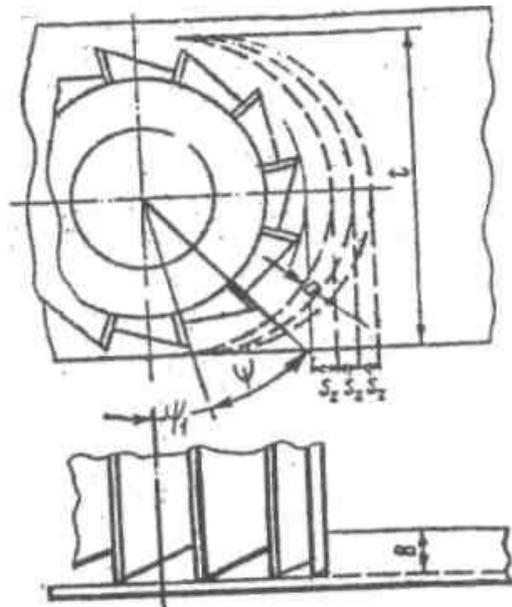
Элементы режима резания при фрезеровании торцевой фрезой
